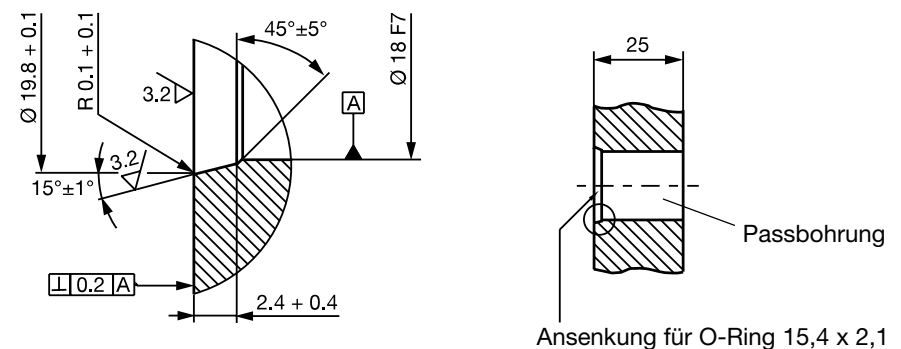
Passbohrung für die Montage des BTL mit O-Ring
